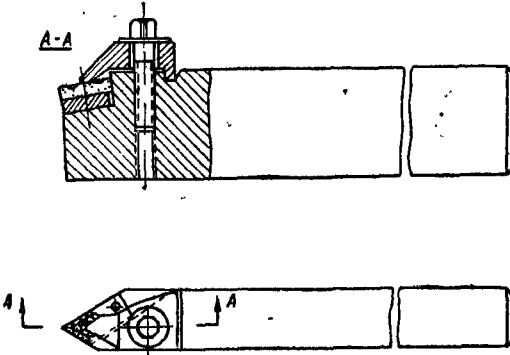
Резьбовой резец с твердосплавной пластинкой ромбической формы.
